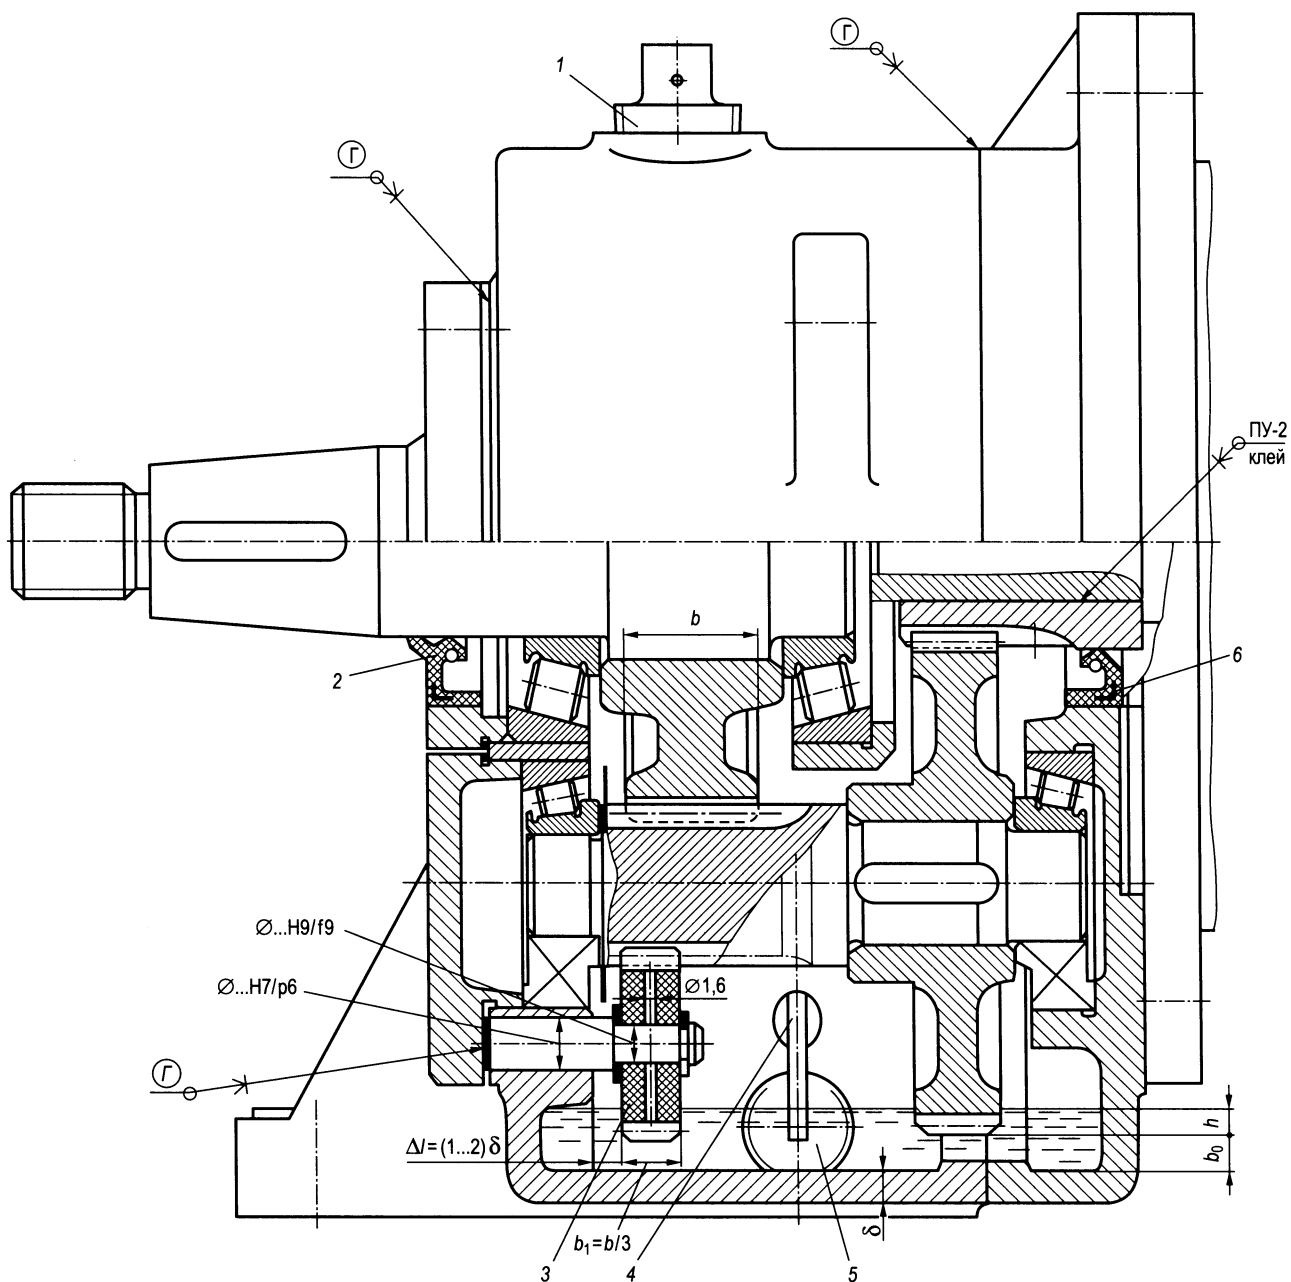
Двухступенчатый соосный мотор-редуктор со смазывающей вспомогательной шестерней:
